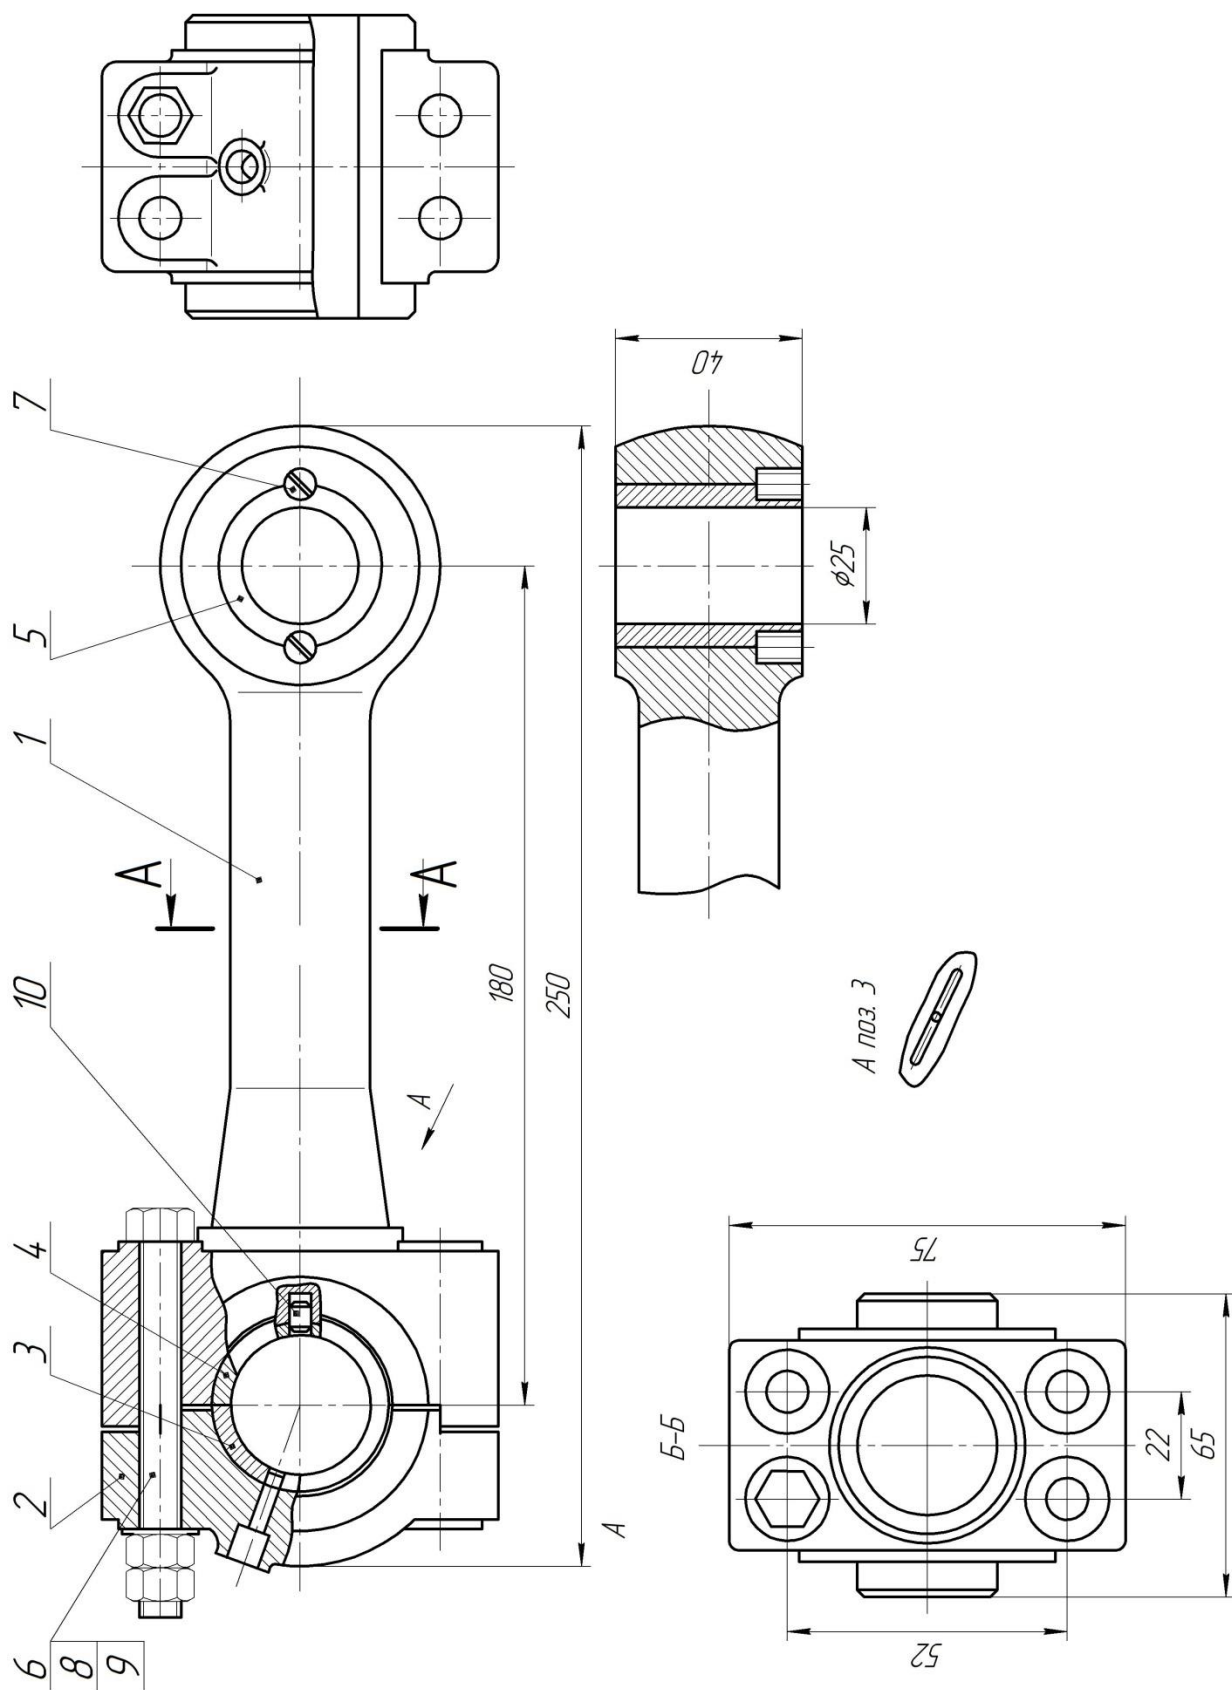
Деталь - «Тяга сборная», общий вид
